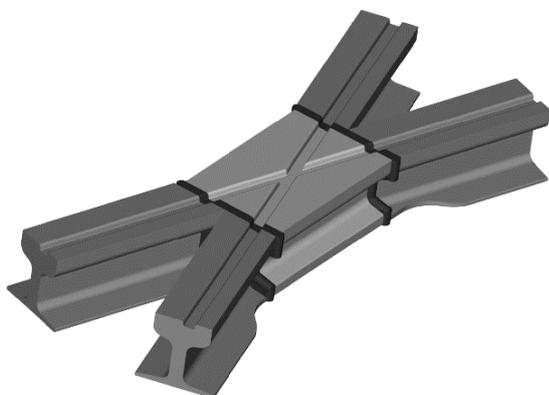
Verbindungsschweissung Anschlusschienen an gefrästen Herzstückblock
